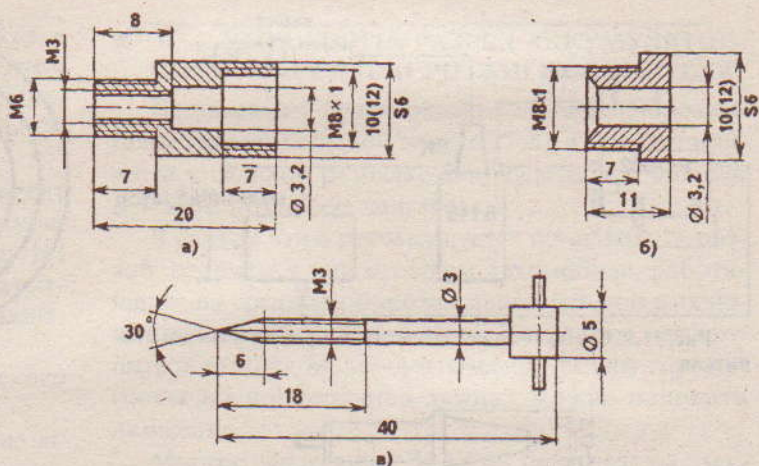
Детали устройства для регулирования подачи топлива в отопитель: а) корпус; б) гайка уплотнения; в) игла
